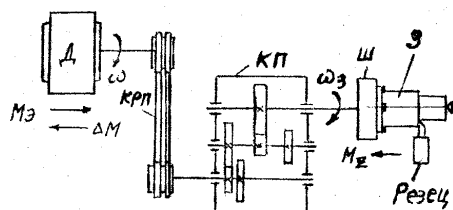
Кинематическая схема ЭП шпинделя токарного станка
